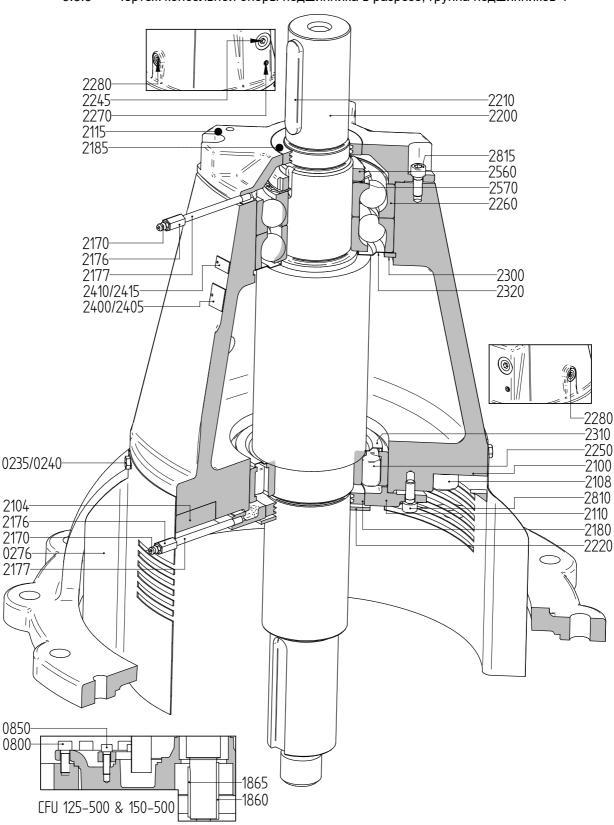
Чертеж консольной опоры подшипника в разрезе, группа подшипников 1-2-3 (A = для группы подшипников 3).
